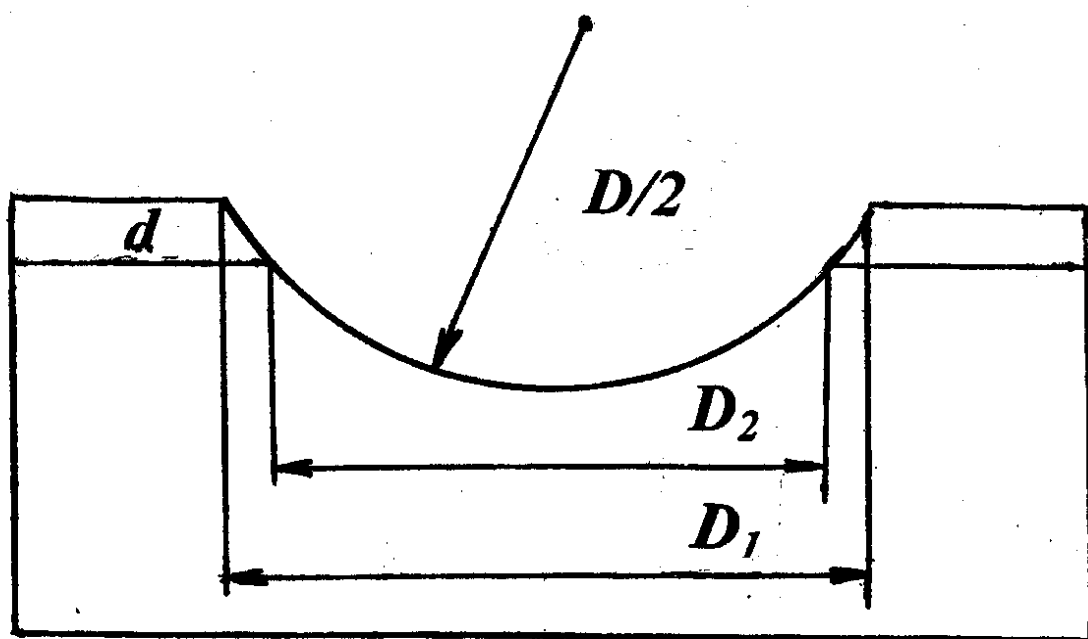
Сферический шлиф пластины с пленкой толщины  $d$
